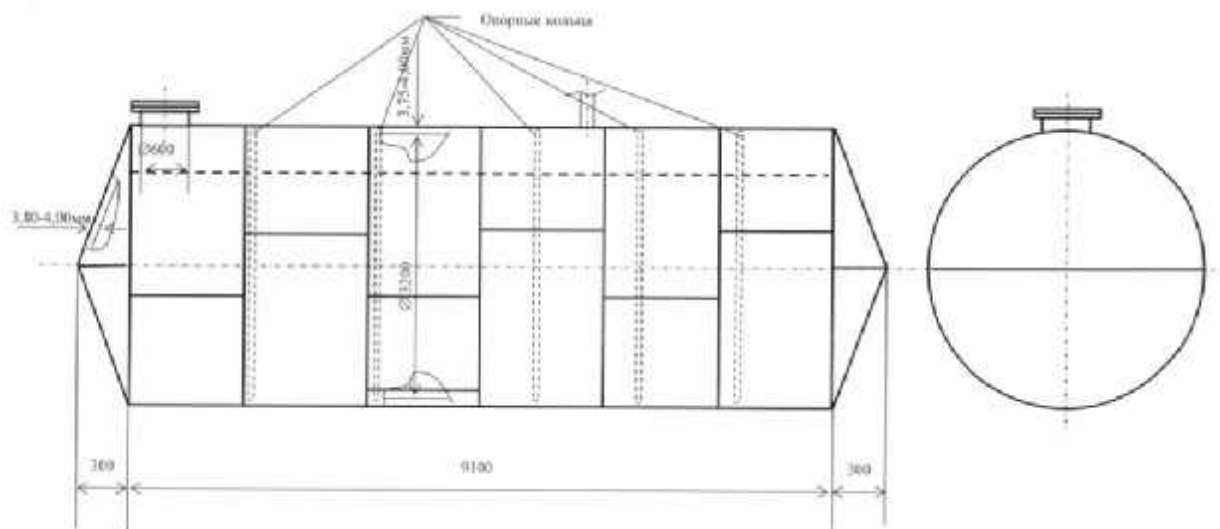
Эскиз резервуара горизонтального стального цилиндрического РГС-75
